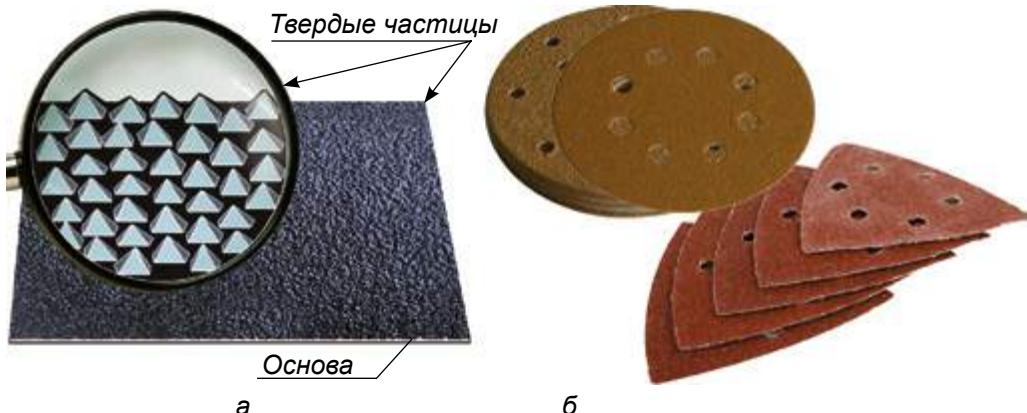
Шлифовальная шкурка: а – схематическое изображение; б – общий вид
